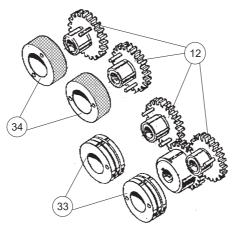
/6с. Запасные ролики для подачи порошковой проволоки / spare part rolls cored wire
